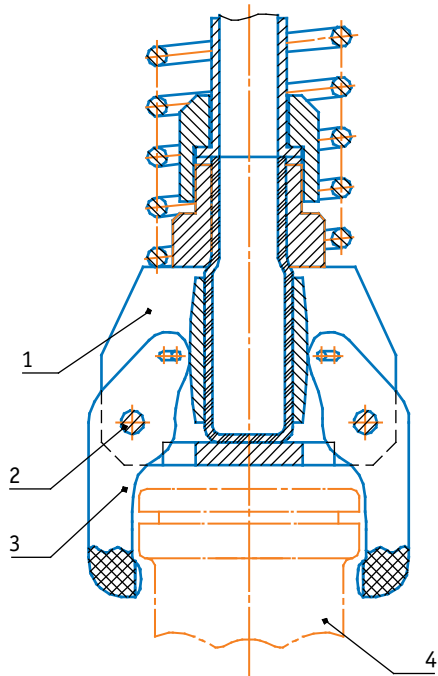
Важільний захоплювальний патрон: 1 — корпус; 2 — вісі; 3 — затискачі; 4 — пляшка
